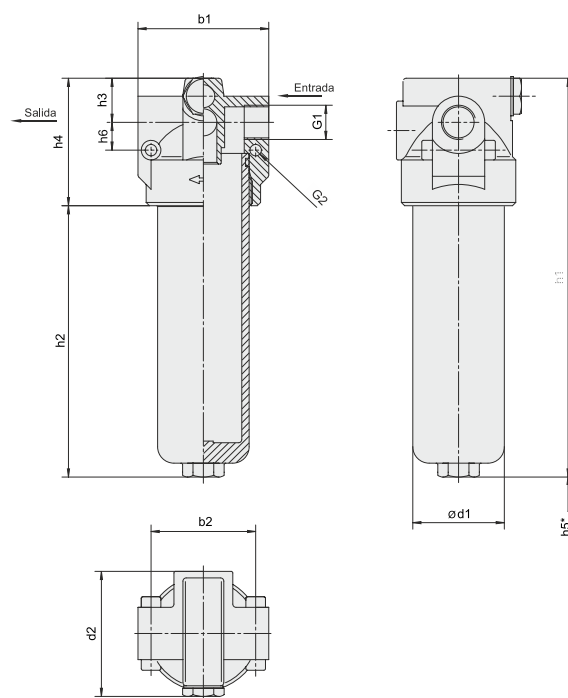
Vistas acotadas del filtro en la línea de impulsión.
